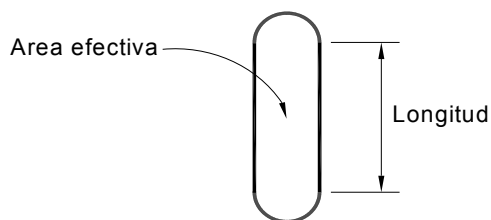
Vista en planta de una soldadura de muesca
